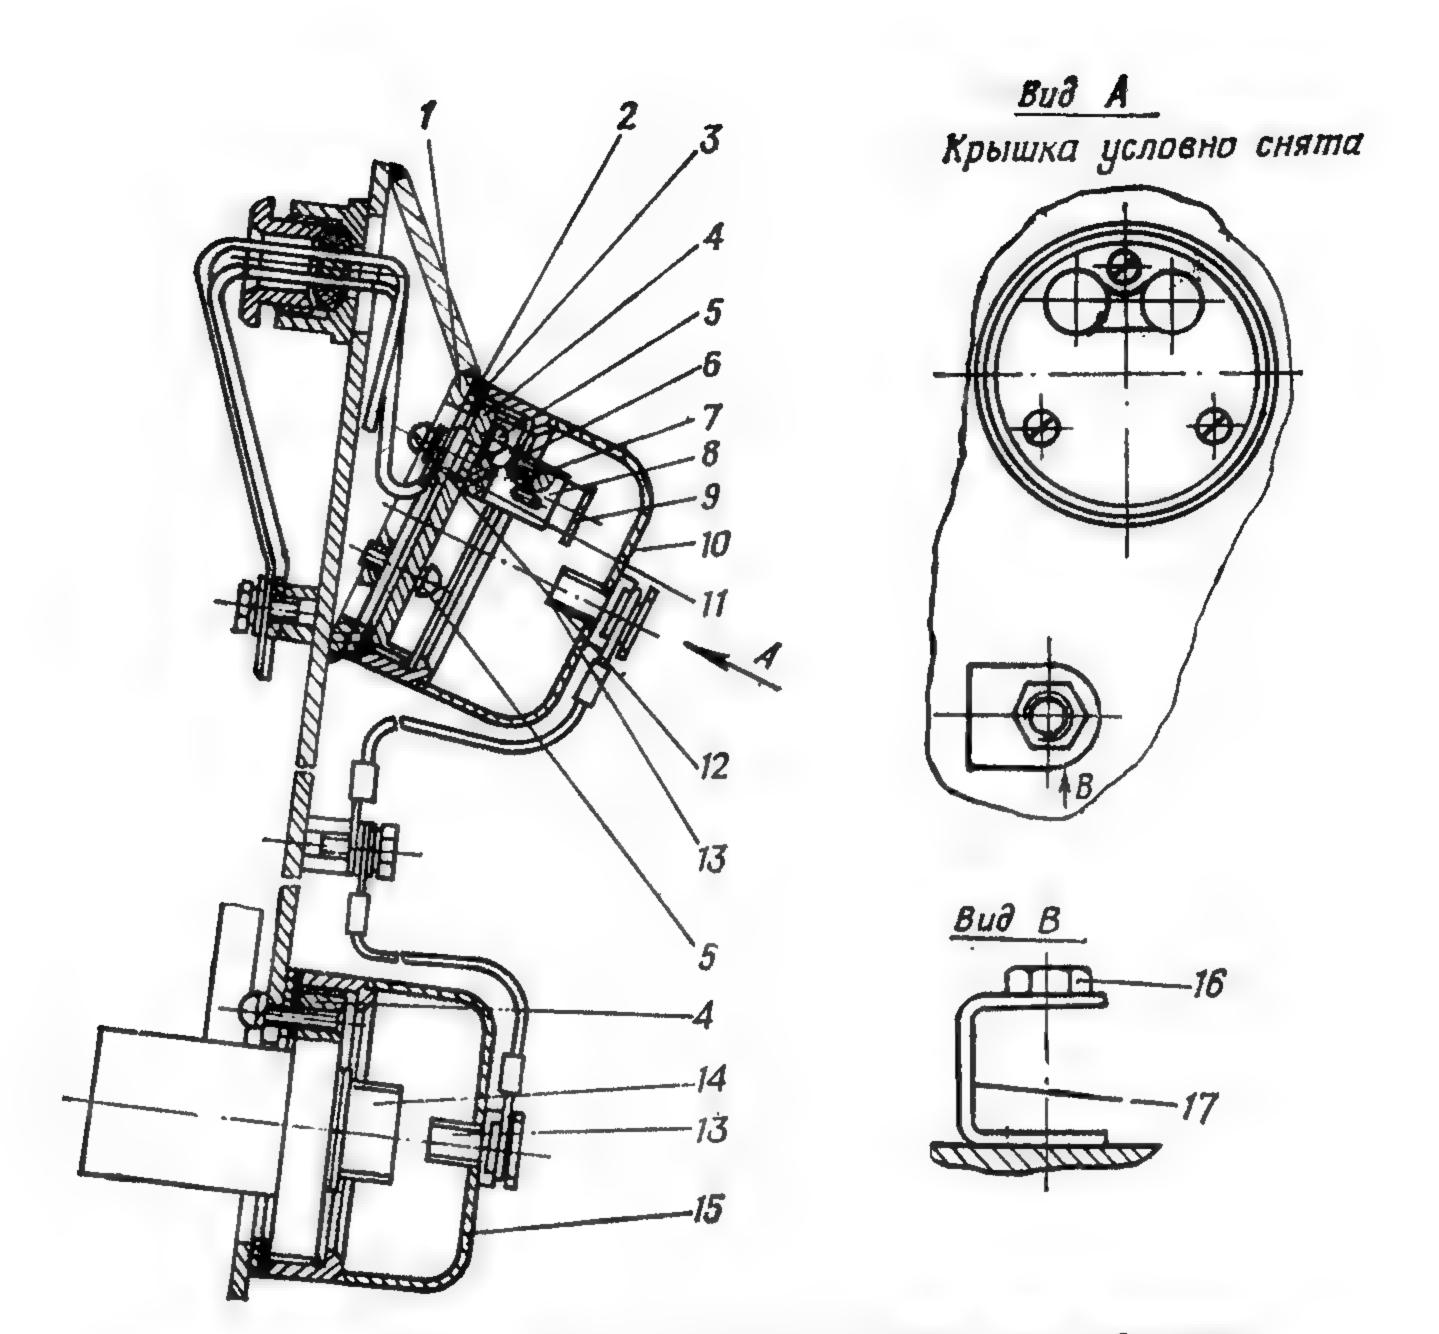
Телефонный ввод и колодка дополнительного абонента: 1. 17— кронштейны; 2— уплотнение; 3— прокладка; 4— плата; 5, 12, 13— винты; 6— изолятор; 7— пружина; 8— зажим; 9— кнопка; 10, 15— крышки; 11— вкладыш; 14— колодка; 16— гайка
